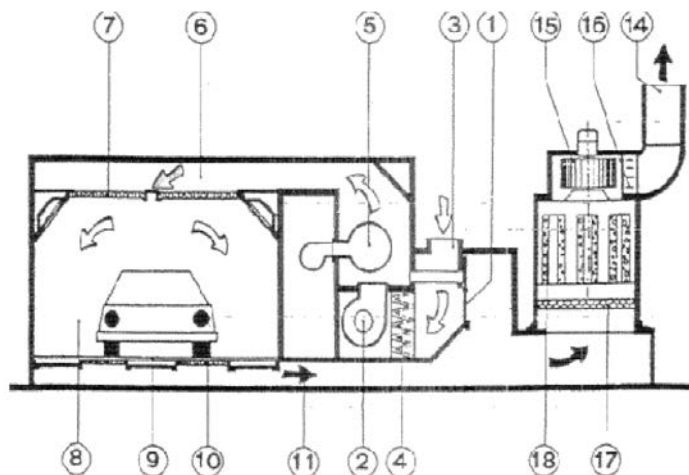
Схема системы с нагнетательным вентилятором на входе и отсасывающим вентилятором на выходе (вентилятор отсасывающий размещен в секции для очистки воздуха с помощью активированного угля)
